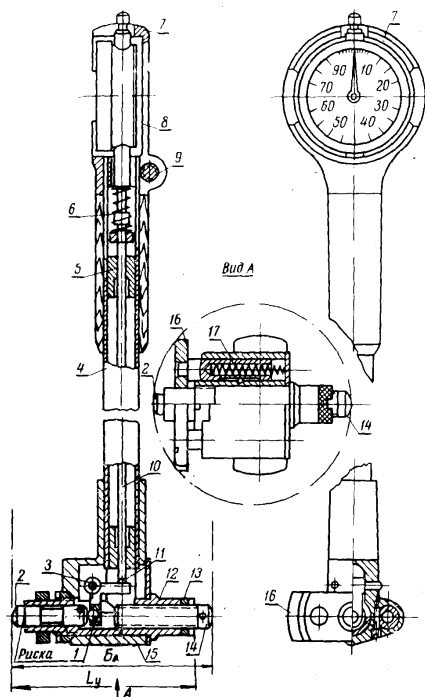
Индикаторный нутромер с рычажной передачей: 1 – шарик; 2 – подвижный стержень; 3 – ось; 4 – трубка; 5 – теплоизоляционная прокладка; 6 – пружина; 7 – кожух; 8 – индикатор; 9 – стопорный винт; 10 – стержень; 11 – двуплечий рычаг; 12 – втулка; 13 – стопорная гайка; 14 – переставной стержень; 15 – корпус; 16 – центрирующий мостик; 17 – пружина
